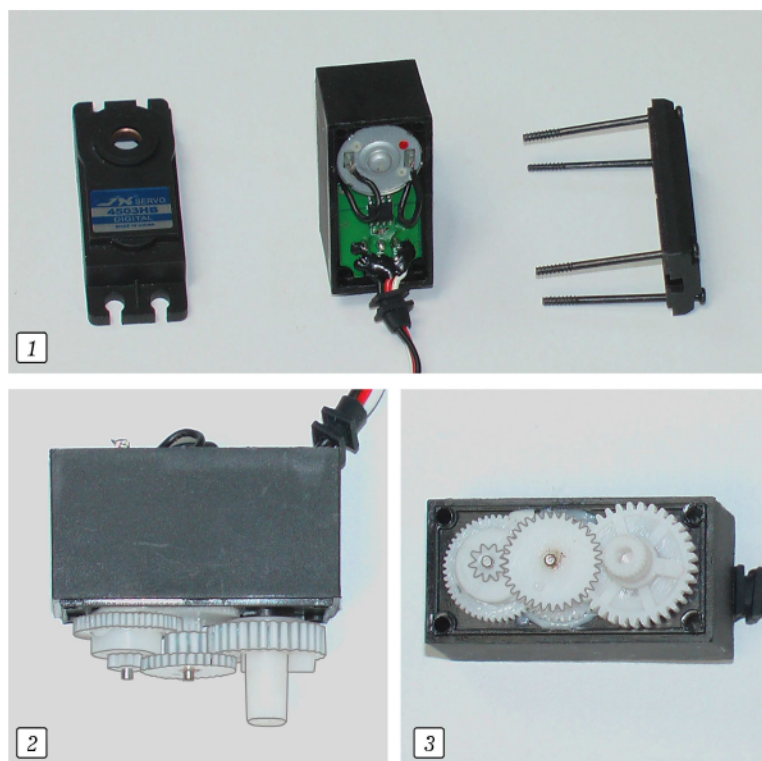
Сервопривод типа 4503HV: 1 — передняя и задняя крышки сняты, в центре показано устройство привода со стороны электродвигателя; 2, 3 — редуктор, вид сбоку и спереди
